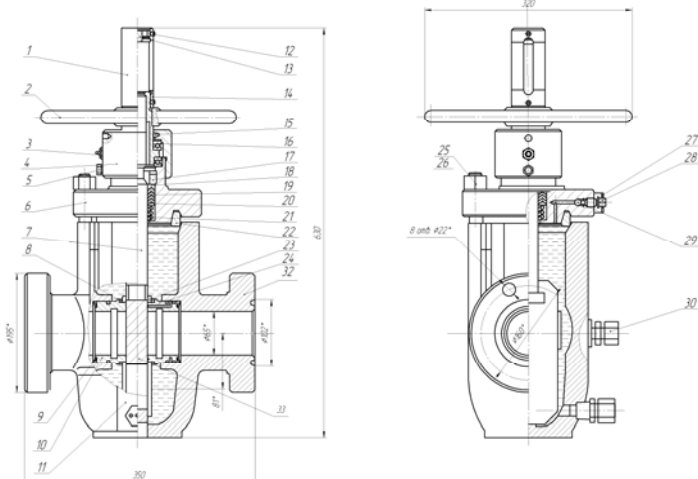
Засувка прямоточна ЗМС1-65×210: 1 – втулка; 2 – штурвал; 3 – мастильниця; 4 – кришка підшипників; 5 – болт М12; 6 – кришка корпусу; 7 – шток; 8 – прокладка; 9 – пружинне кільце; 10 – шочка; 11 – напрямні; 12 – фіксатор; 13 – регулювальний гвинт; 14 – ковпак; 14 – втулка дистанційна; 15 – прокладка; 16 – підшипник; 18 – кільце натискне верхнє; 19 – ущільнення; 20 – кільце натискне нижнє; 21 – пружина; 22 – прокладка ущільнююча; 23 – втулка напрямна; 24 – сідло; 25 – шпилька М25; 26 – гайка М25; 27 – кришка прес-мастильниці; 28 – прес-мастильниця; 29 – кулька; 30 – гвинт натискний; 32 – корпус; 33 – шибєр
